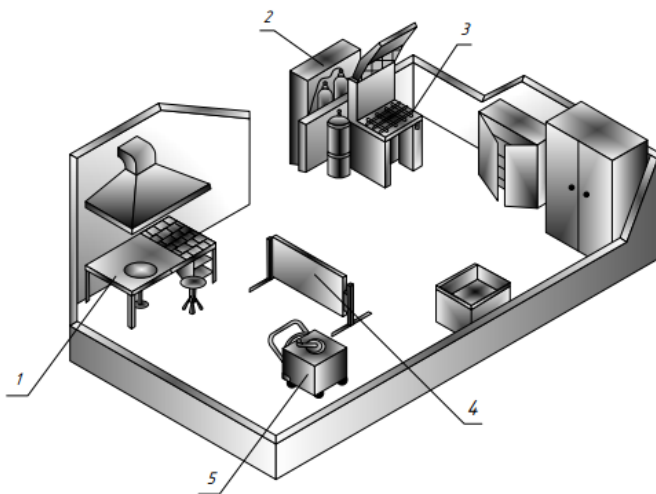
Сварочно-наплавочный участок:
